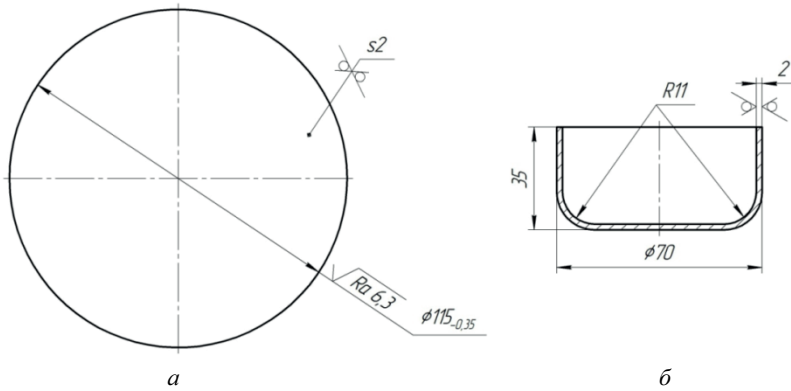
Чертеж заготовки (а) и готовой детали (б)
